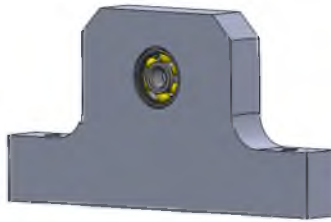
Ensamble en CAD del rodamiento y la chumacera.
